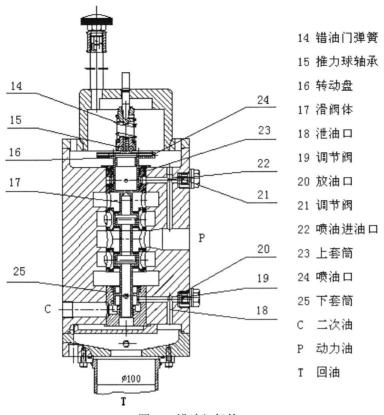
错油门机构 Fig. 3.6 pilot valve mechanism
